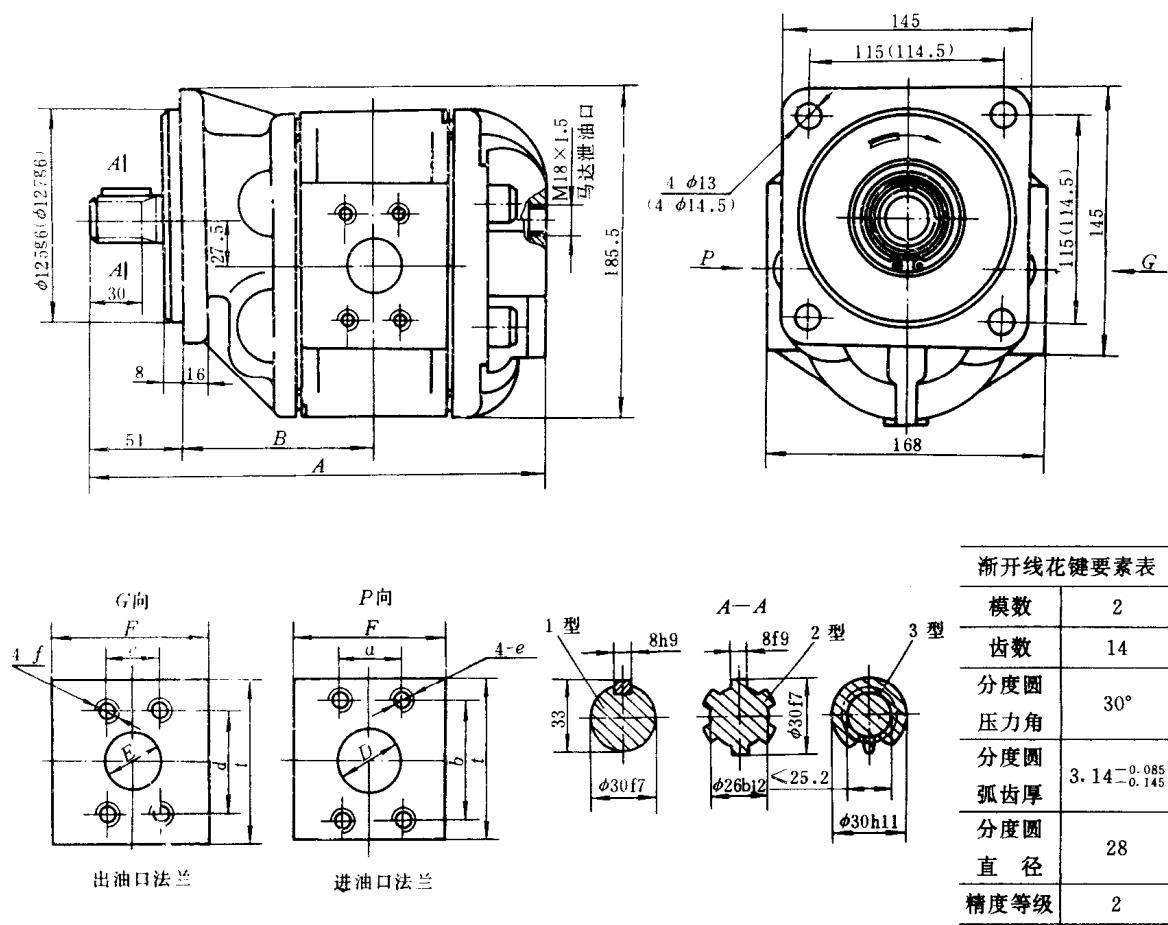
CBG2 (CMG2) 齿轮泵 (齿轮马达)
